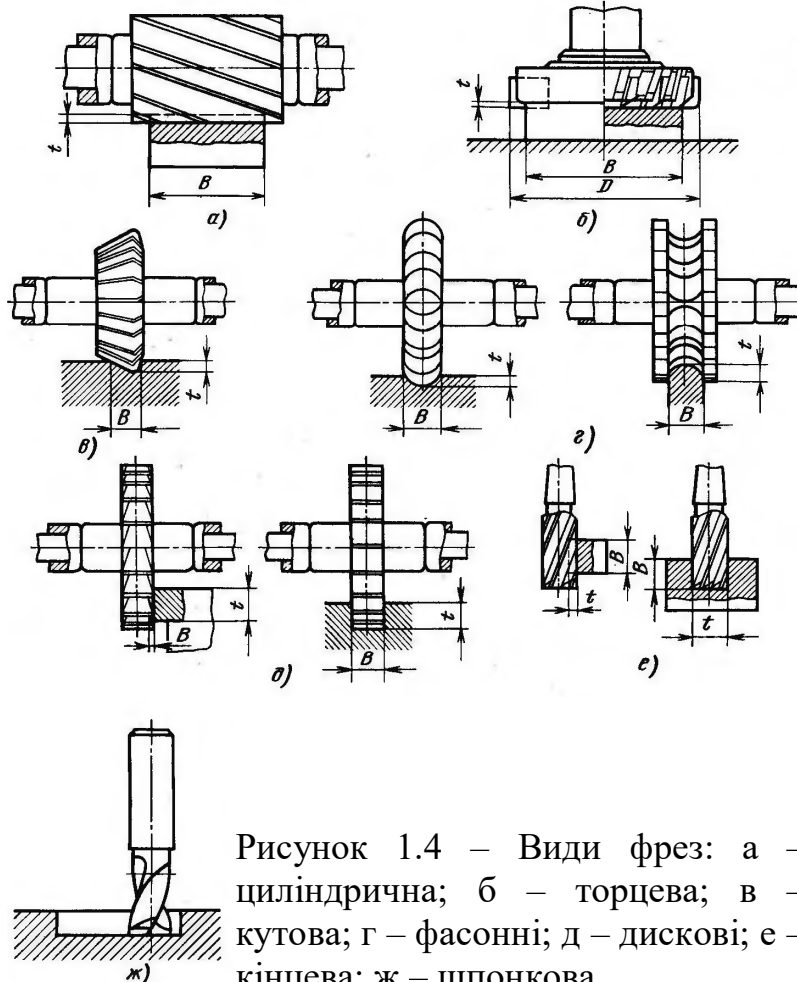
Види фрез: а – циліндрична; б – торцева; в – кутова; г – фасонні; д – дискові; е – кінцева; ж – шпонкова
